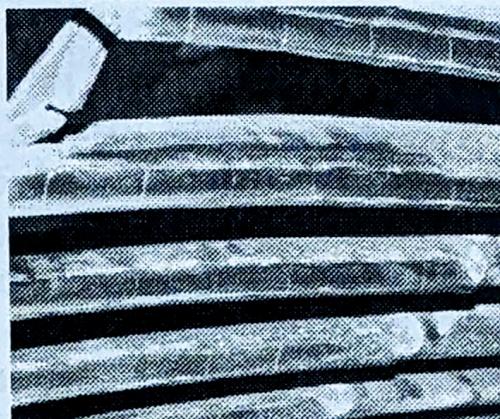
Внешний вид лопаток после приварки стеллитовых пластин
